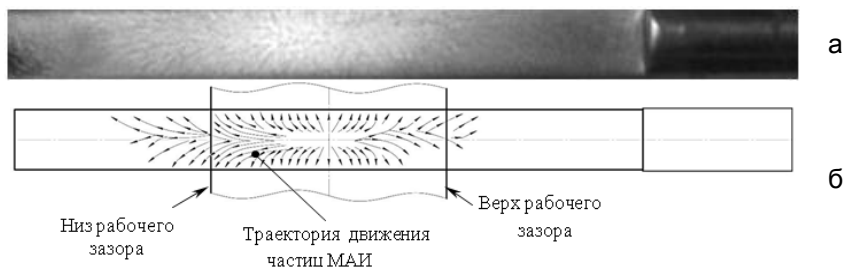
Внешний вид контрольной поверхности образца после МАО – а и схематическое представление движения частичек МАИ в процессе обработки – б
